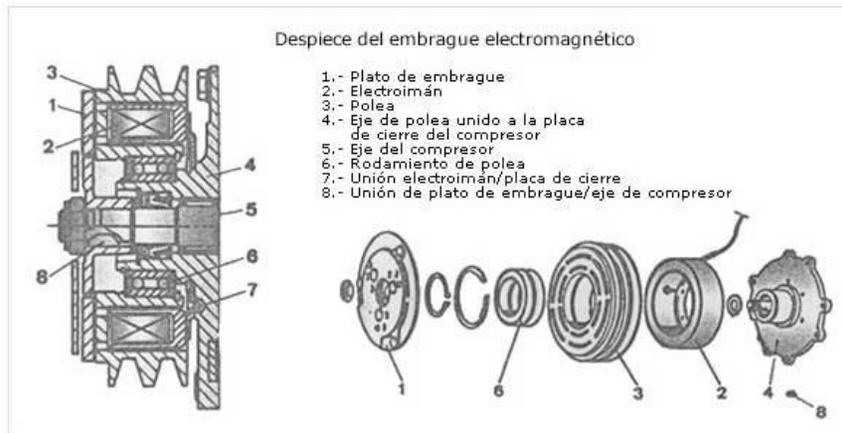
DESPIECE DEL EMBRAGUE MAGNÉTICO²⁰
